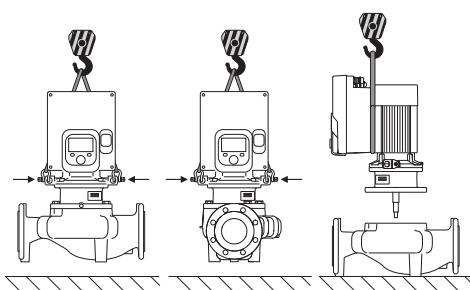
Směr zdvihání se svislou hřídelí motoru
